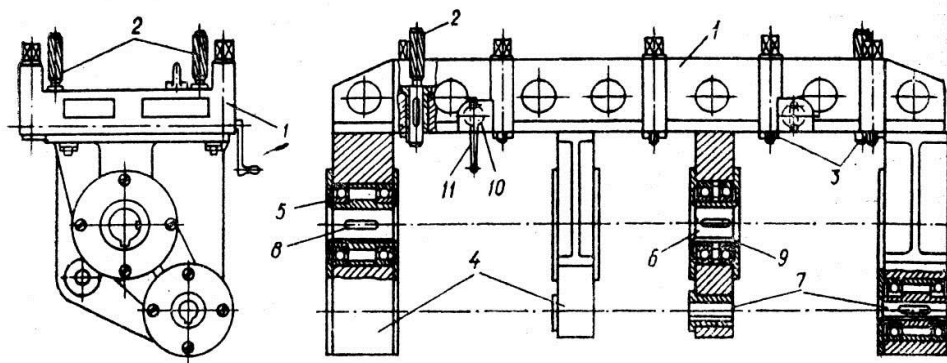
Пристрій (кондуктор) для розточування гнізд корінних підшипників блока циліндрів:
